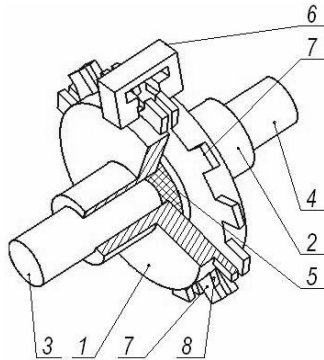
Схема стенду для випробувань конічно – циліндричного редуктора розкидача твердих органічних добрив
